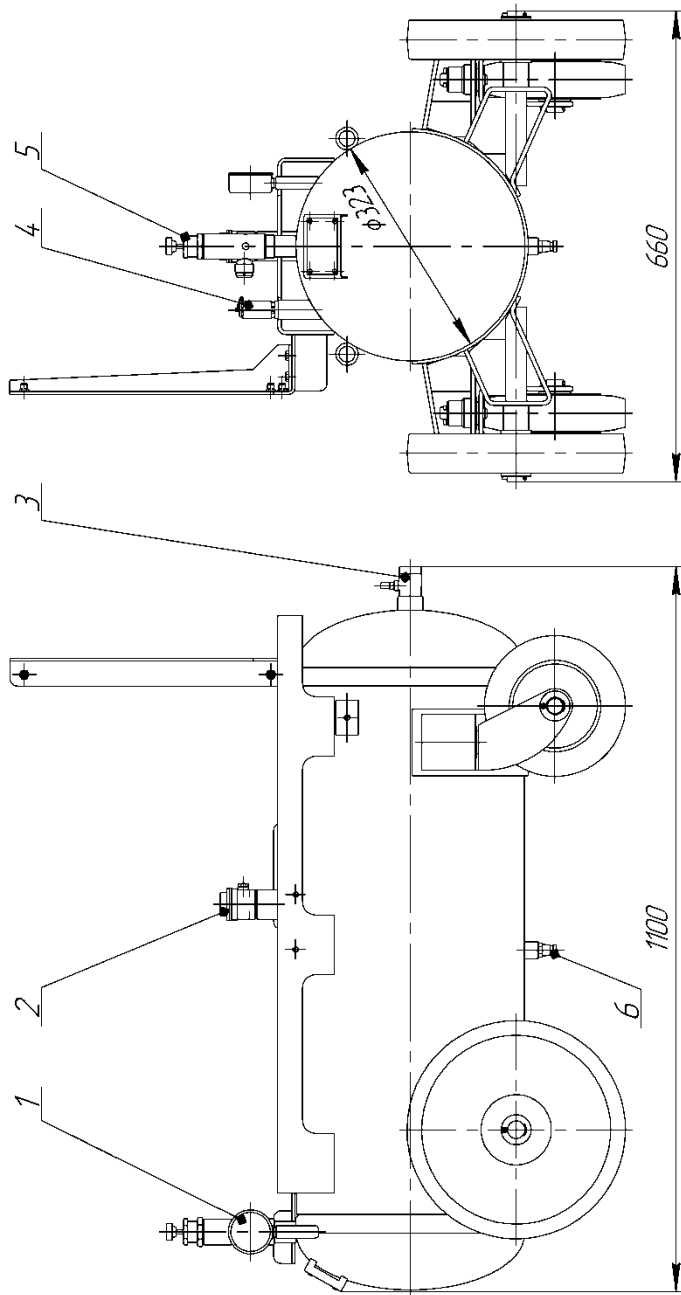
Ресивер установки компрессорной, модель К-30:
